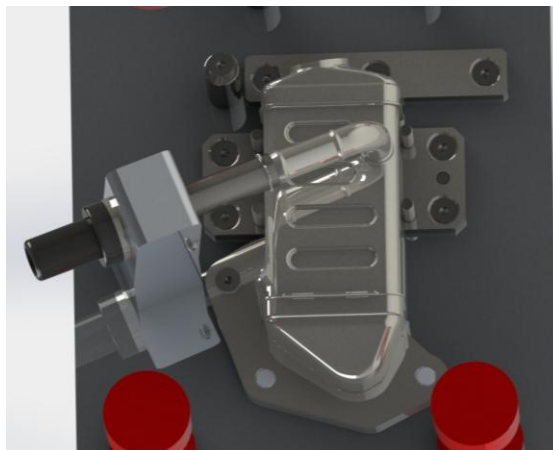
Utillaje de soldadura láser de fase 3. Posición de soldeo de tubo de refrigeración de agua.
